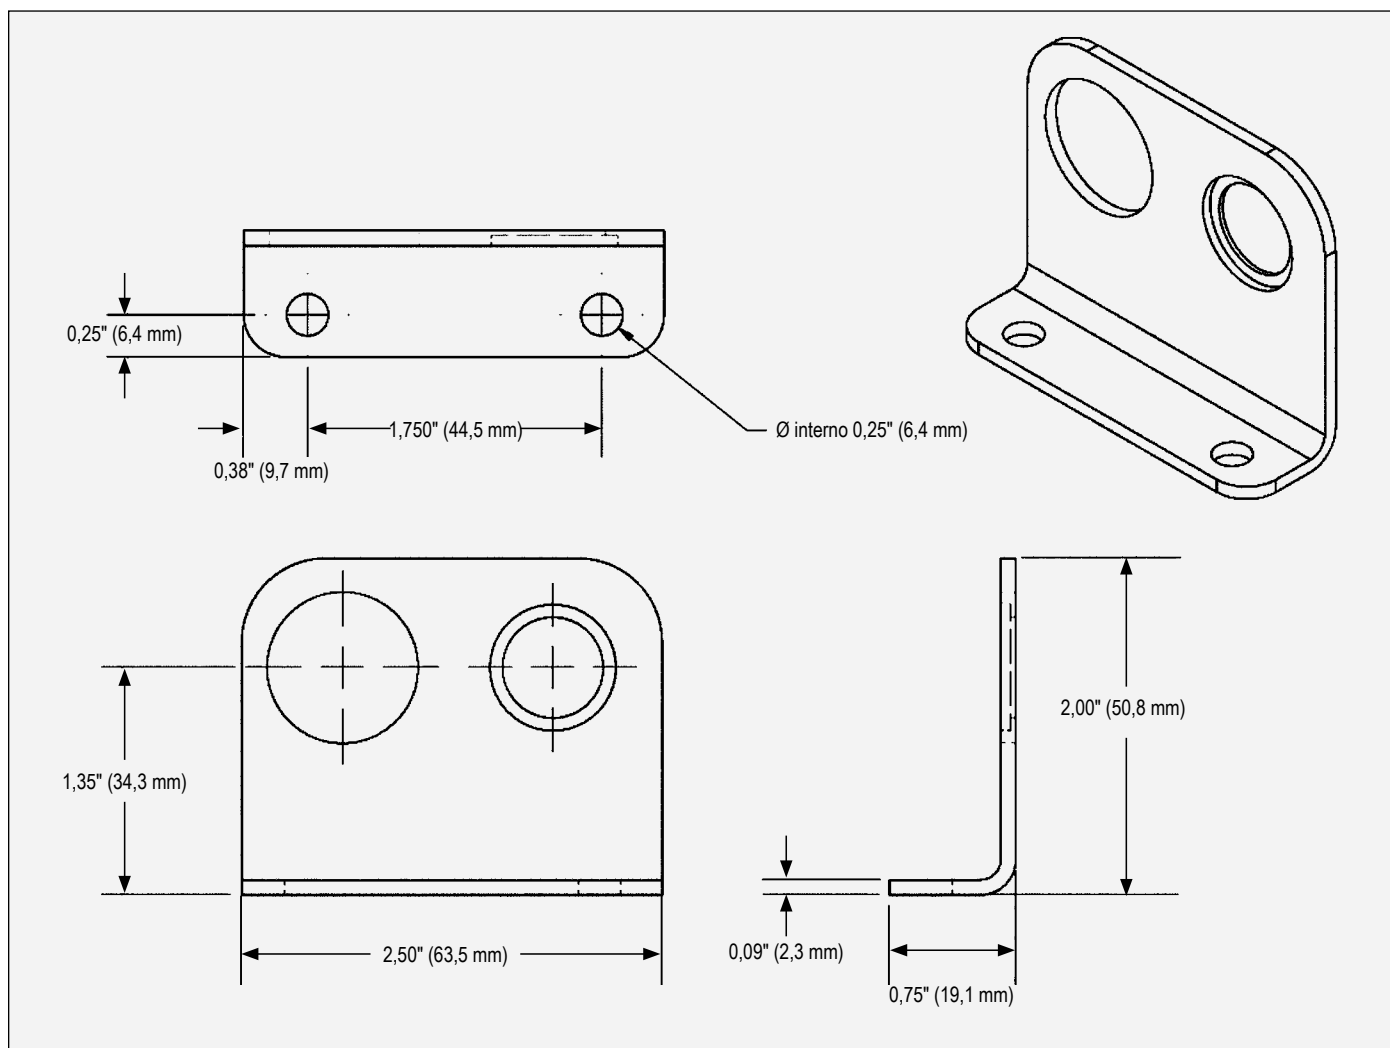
Dimensioni della squadra di fissaggio del cavo LV
